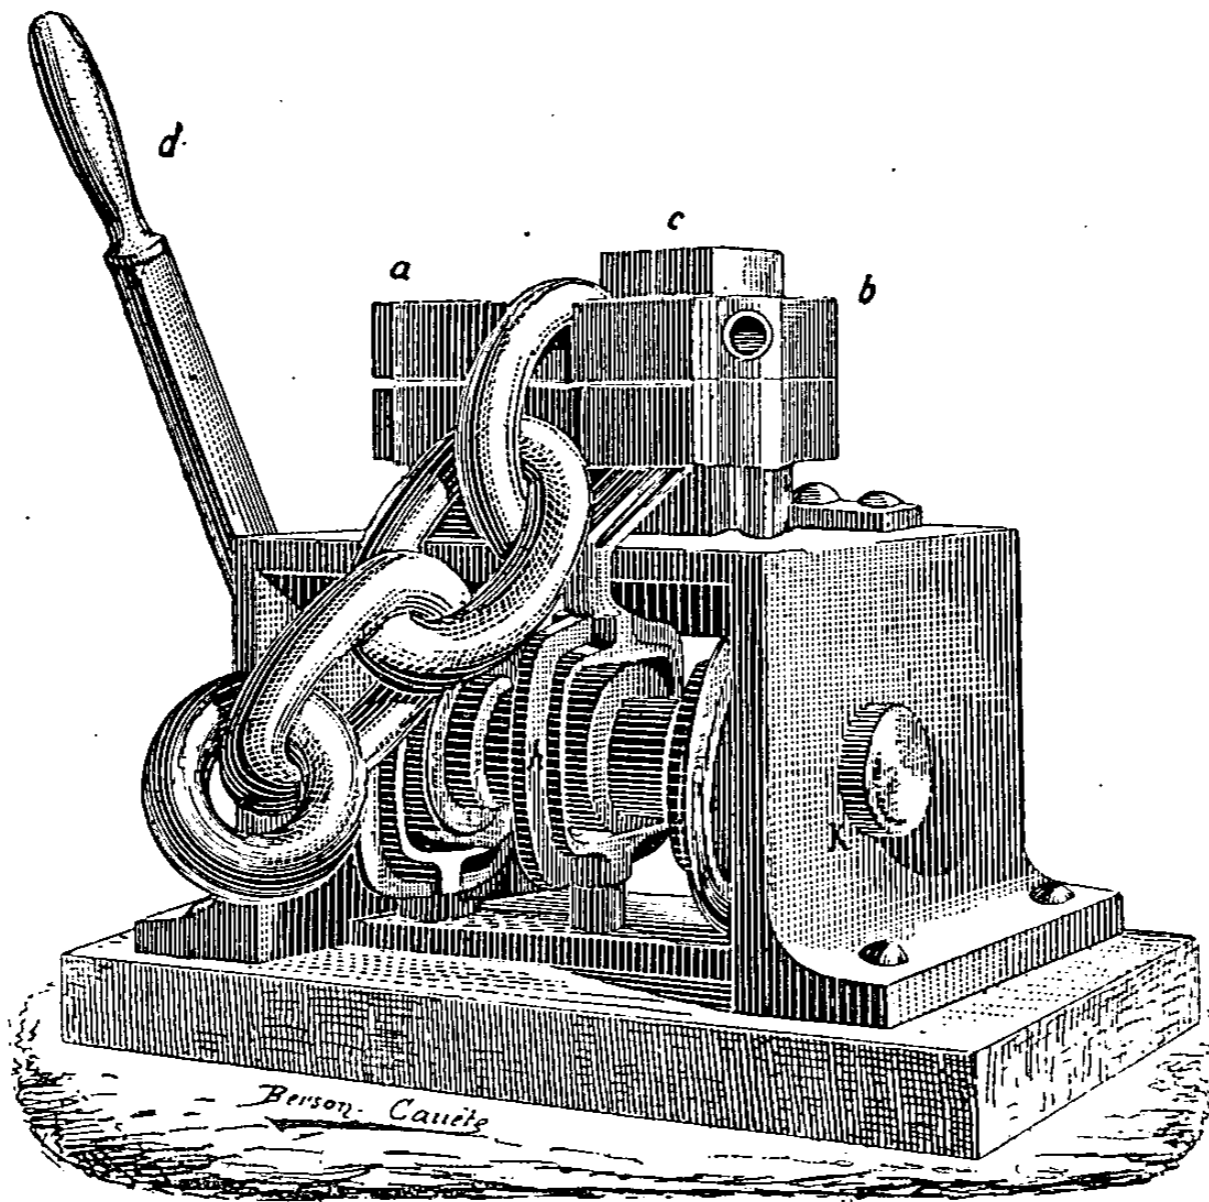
Fabrication des chaînes en acier coulé, procédé Imbert et Léger.
